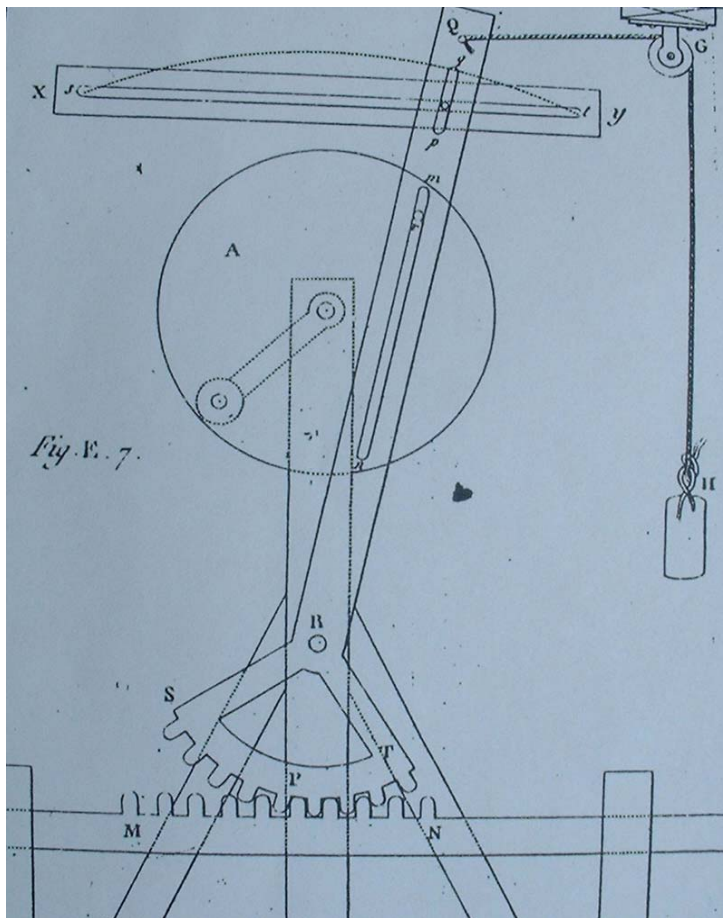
, page 62 et planche N°2, Lanz et Bétancourt.
